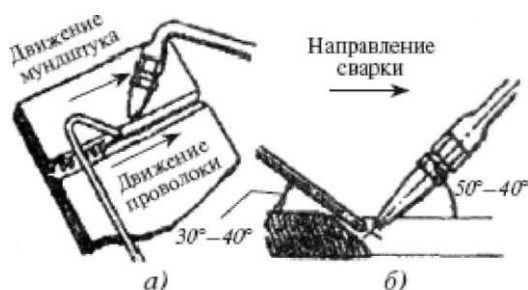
Правая сварка: а - схема движения мунштука и горелки; б - углы наклона мунштука и проволоки
